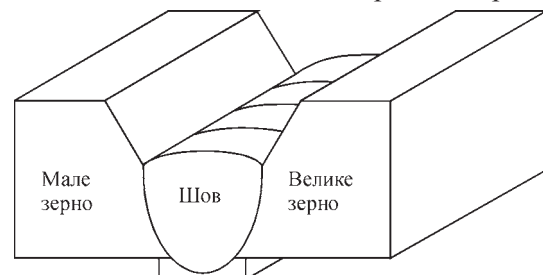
Схема зварного з'єднання з різним розміром зерен
